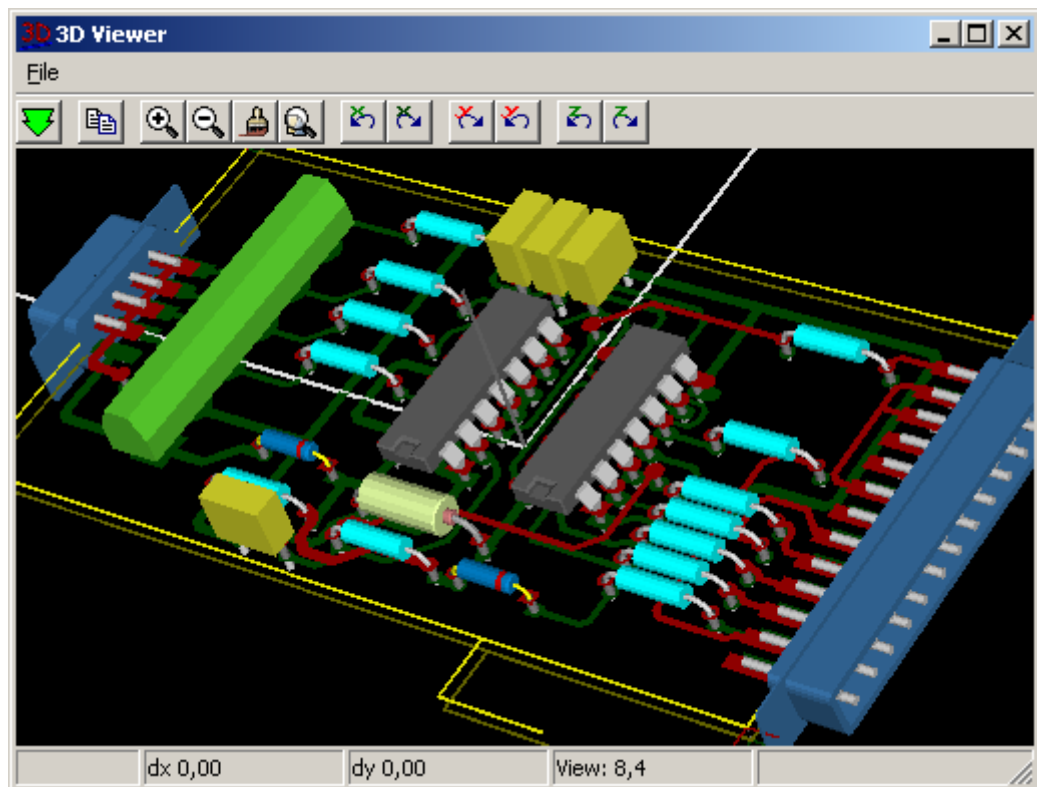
Тривимірний вигляд друкованої плати у 3D Viewer pcbnew
